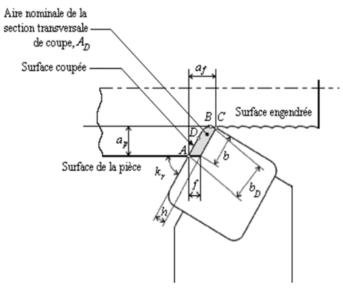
Dimensions de coupe dans le cas de tournage. [13]
